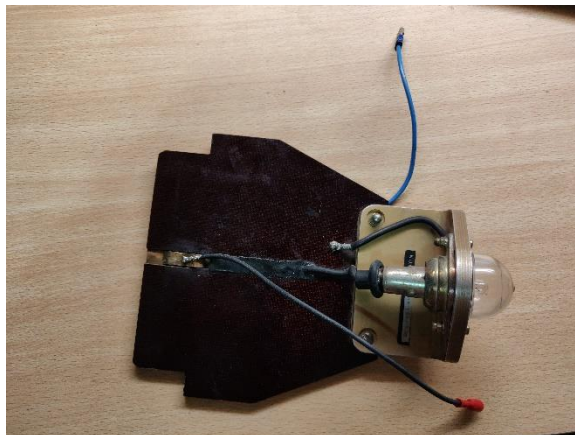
Cable soldado en el polo positivo de la Tarjeta de tiro. Fuente: elaboración propia.
